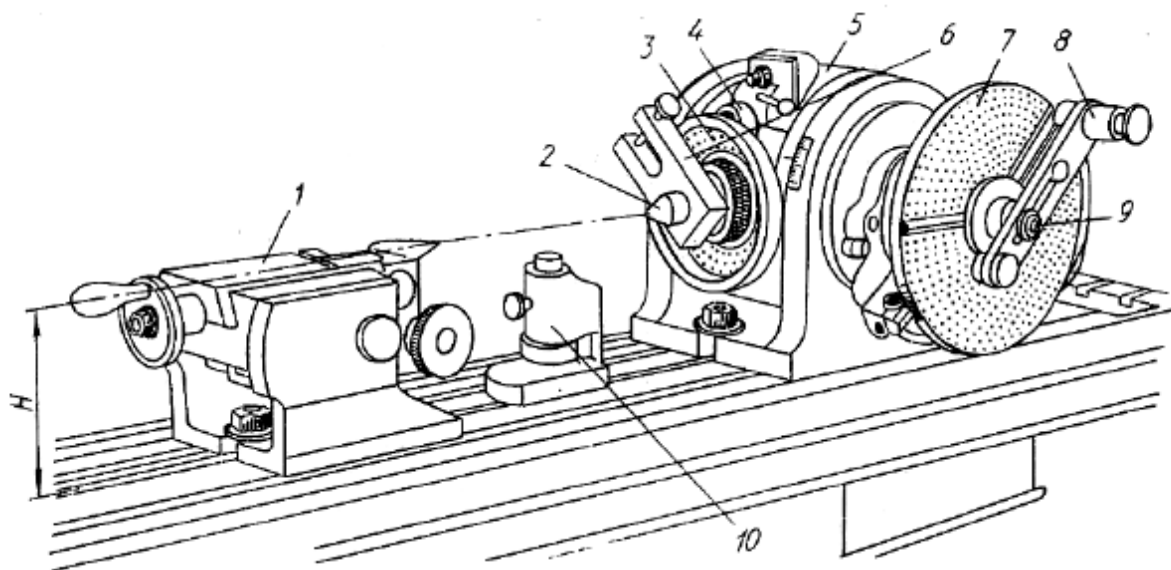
Універсальна ділильна головка: 1 - задня бабка; 2 - центр; 3 - лобовий диск; 4 - фіксатор; 5 - колодка; 6 - поводок; 7 - ділильний диск; 8 -
